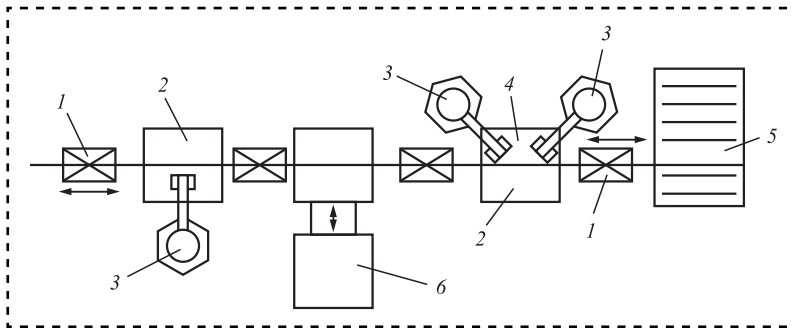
Схемы основных устройств транспортной системы линии сборки-сварки кузовов:
